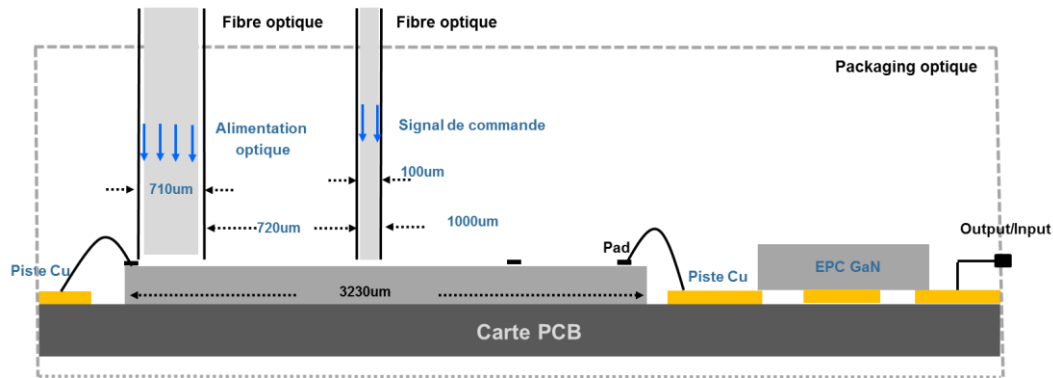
Assemblage de la puce CMOS AMS C35 avec le PCB et packaging optique.
